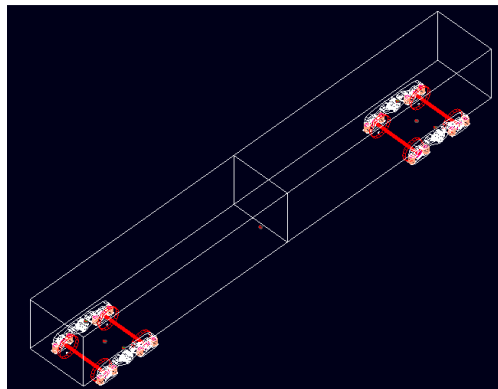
Ensamblado del conjunto caja-bogieY25
